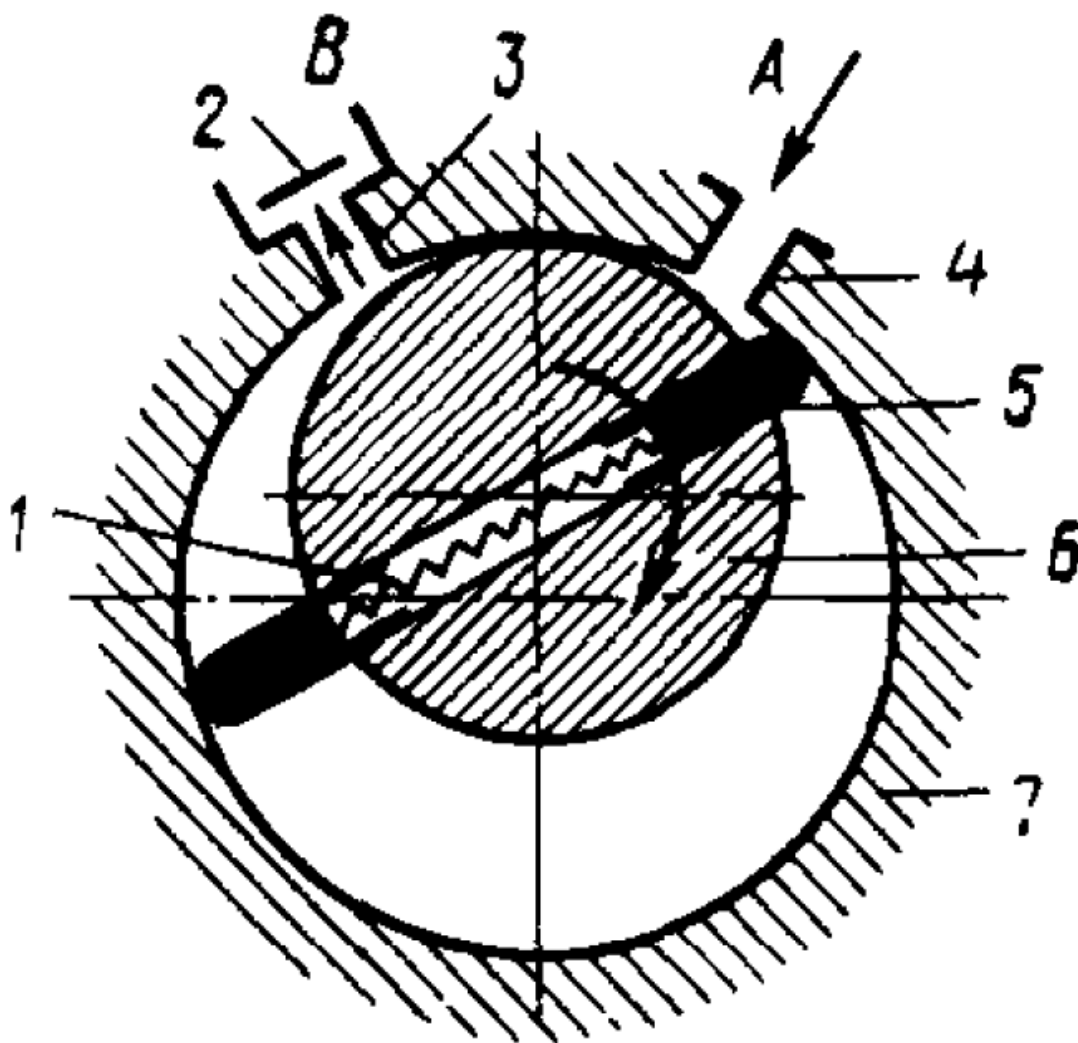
Устройство пластинчато-роторного насоса. 1 – пружина; 2 – клапан; 3 – выхлопной патрубок; 4 – впускной патрубок; 5 – пластины; 6 – ротор; 7 – цилиндрический корпус [7, с. 165]
